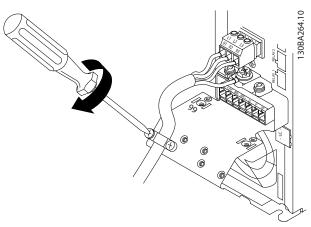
Apriete la abrazadera de montaje de los cables de red.
